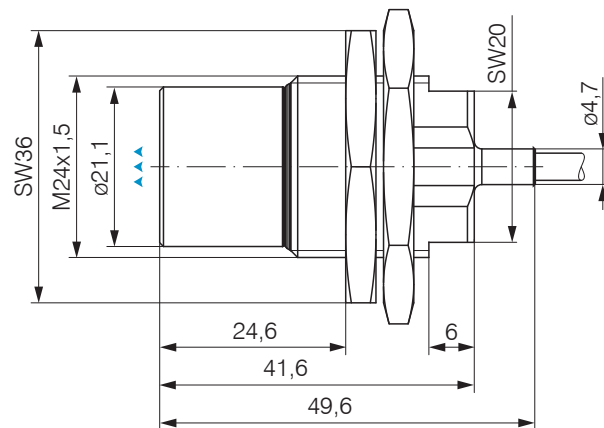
Maßzeichnung Sensoren ES-U8-C-CaX/mB0
